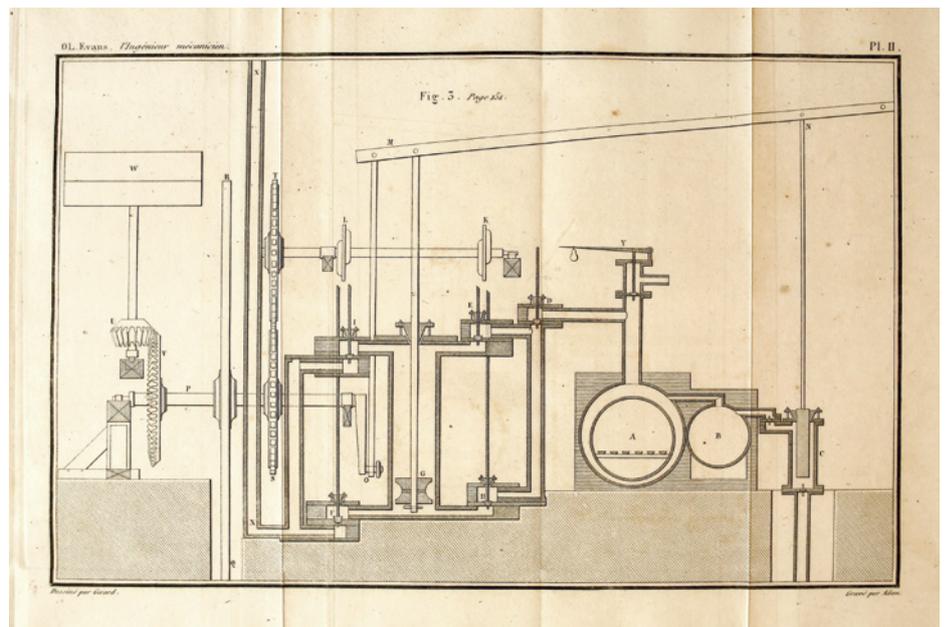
Oliver Evans: Manuel de l'ingénieur mécanicien constructeur de machines à vapeur. 1825. Tafel II
